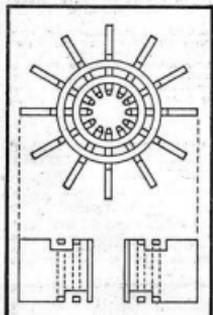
Vue en plan et coupe de la cavité résonnante, montrant les deux sections en culvres.
